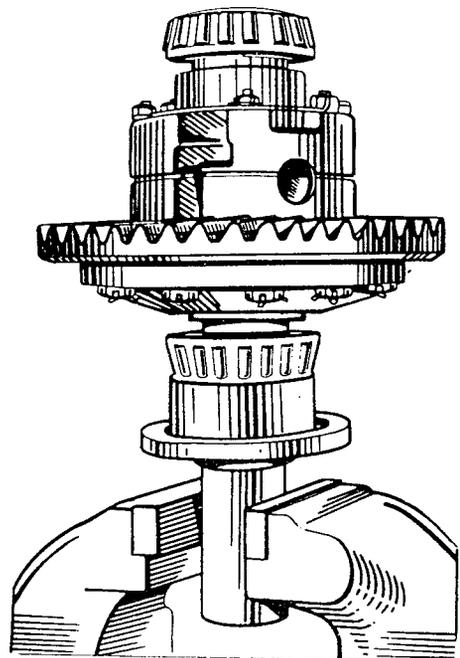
Aufpressen der Lagerinnenringe des Ausgleichgetriebes
